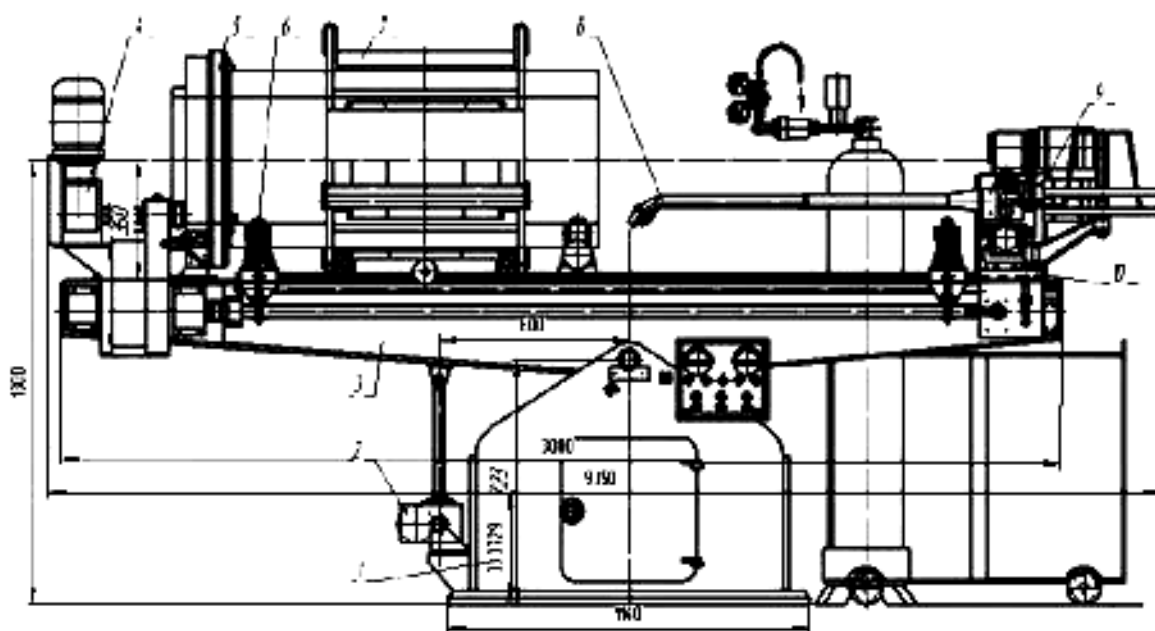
Верстат Р922-Г для наплавлення внутрішніх циліндричних поверхонь
